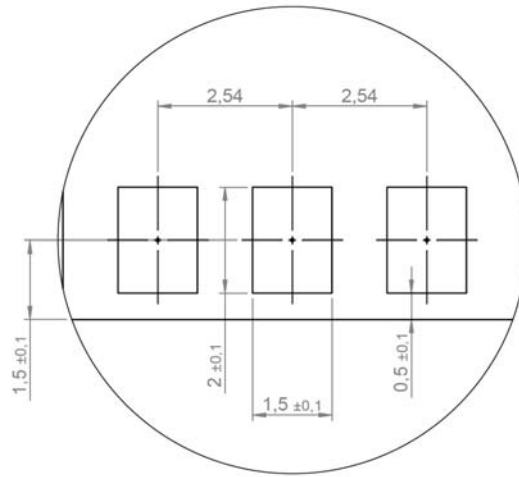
Dimensioni della pad per il contatto tramite SDI [dimensioni in mm]
